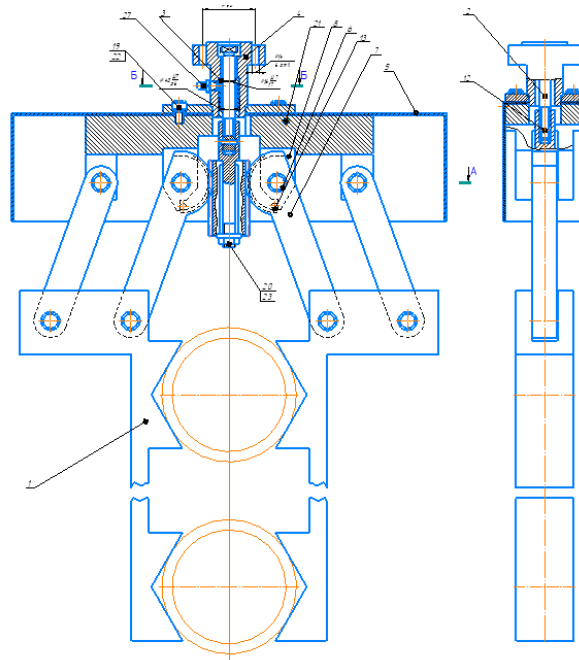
Жорсткий захватний пристрій для захоплення циліндричних елементів
